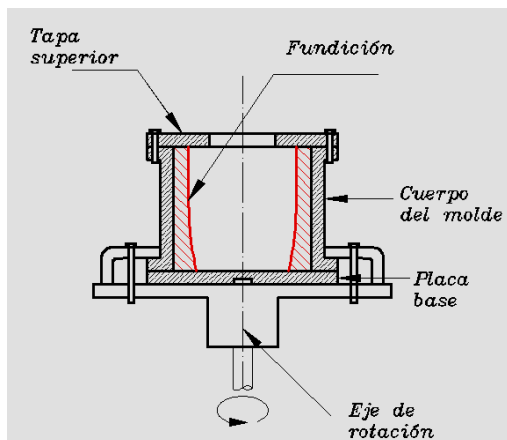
ESQUEMA DE LOS COMPONENTES DE UN MOLDE METÁLICO PARA FUNDICIÓN CENTRÍFUGA
